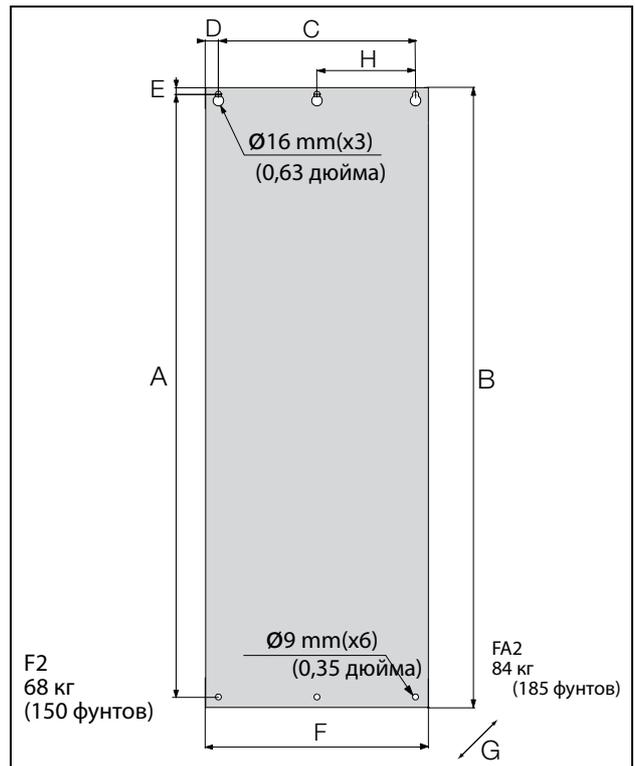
Устройство /FDU моделей от 48-205 до 48-293 (размер корпуса F2) и 48-365-20 (размер корпуса FA2).
